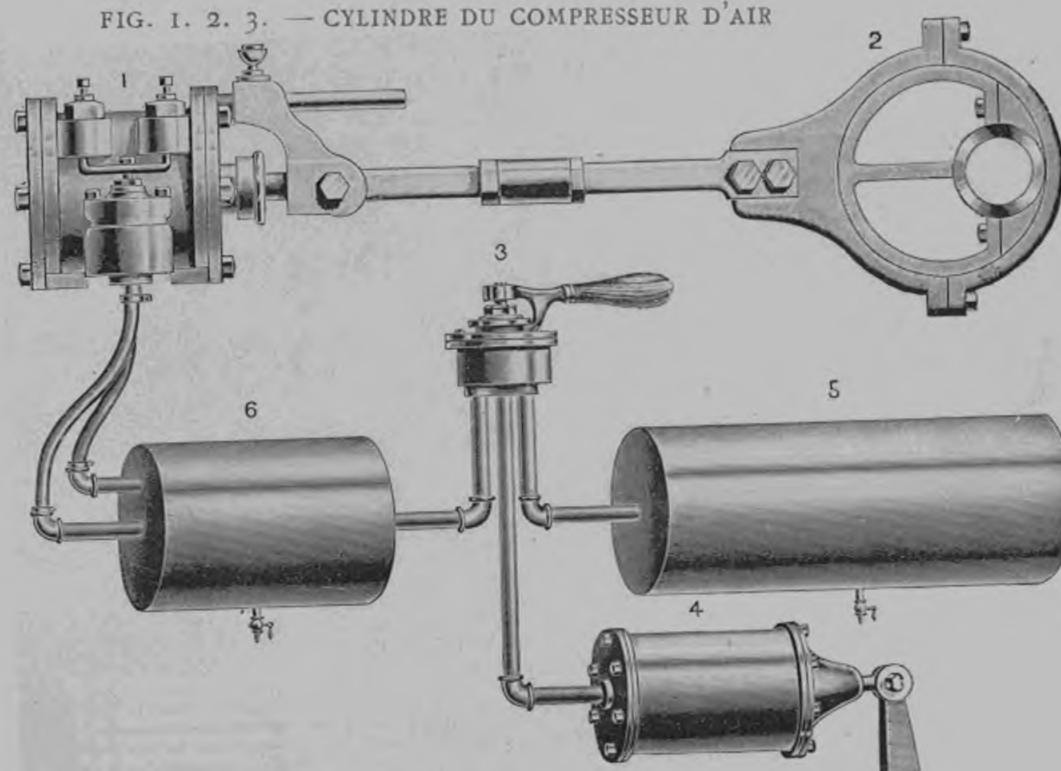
ENSEMBLE DU MONTAGE DU FREIN
